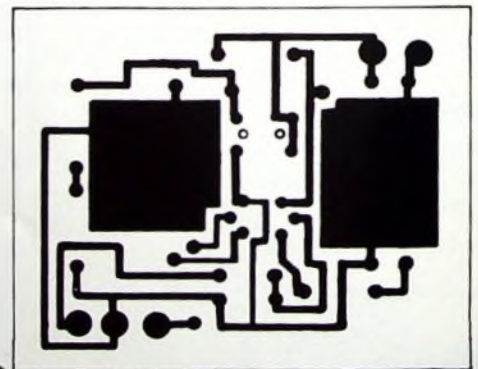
Printzeichnung des NF-Teils (Maßstab 1:1)
